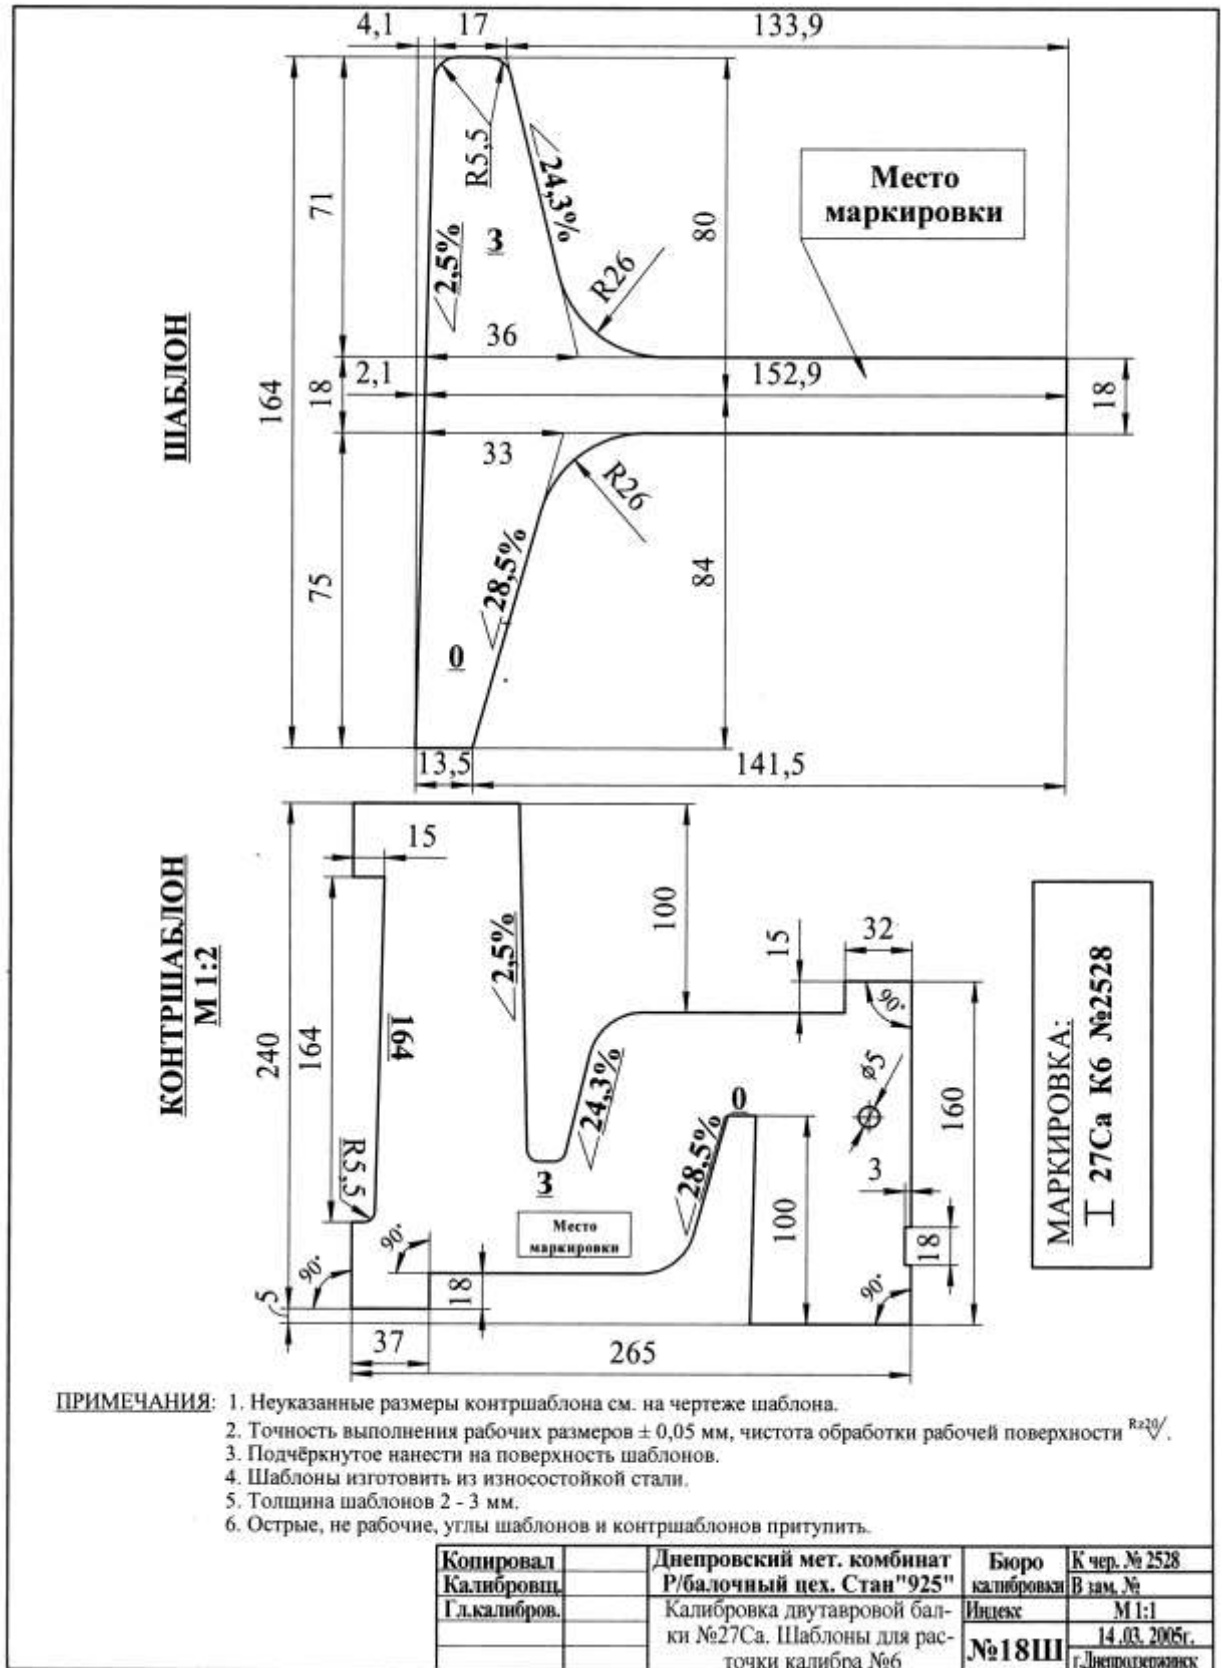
Креслення шаблону та контршаблону для розточування калібру №6 згідно калібровки валків для прокатування двотаврової балки №27Са
